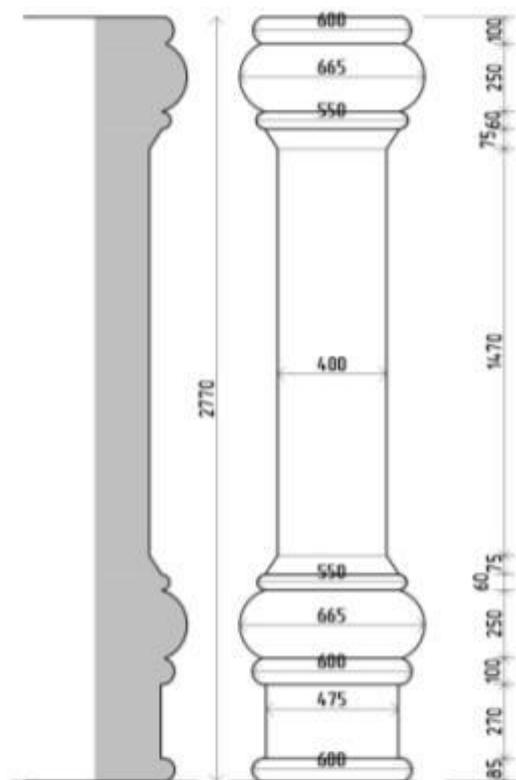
Габаритные размеры левой колонны гардеробной стойки
